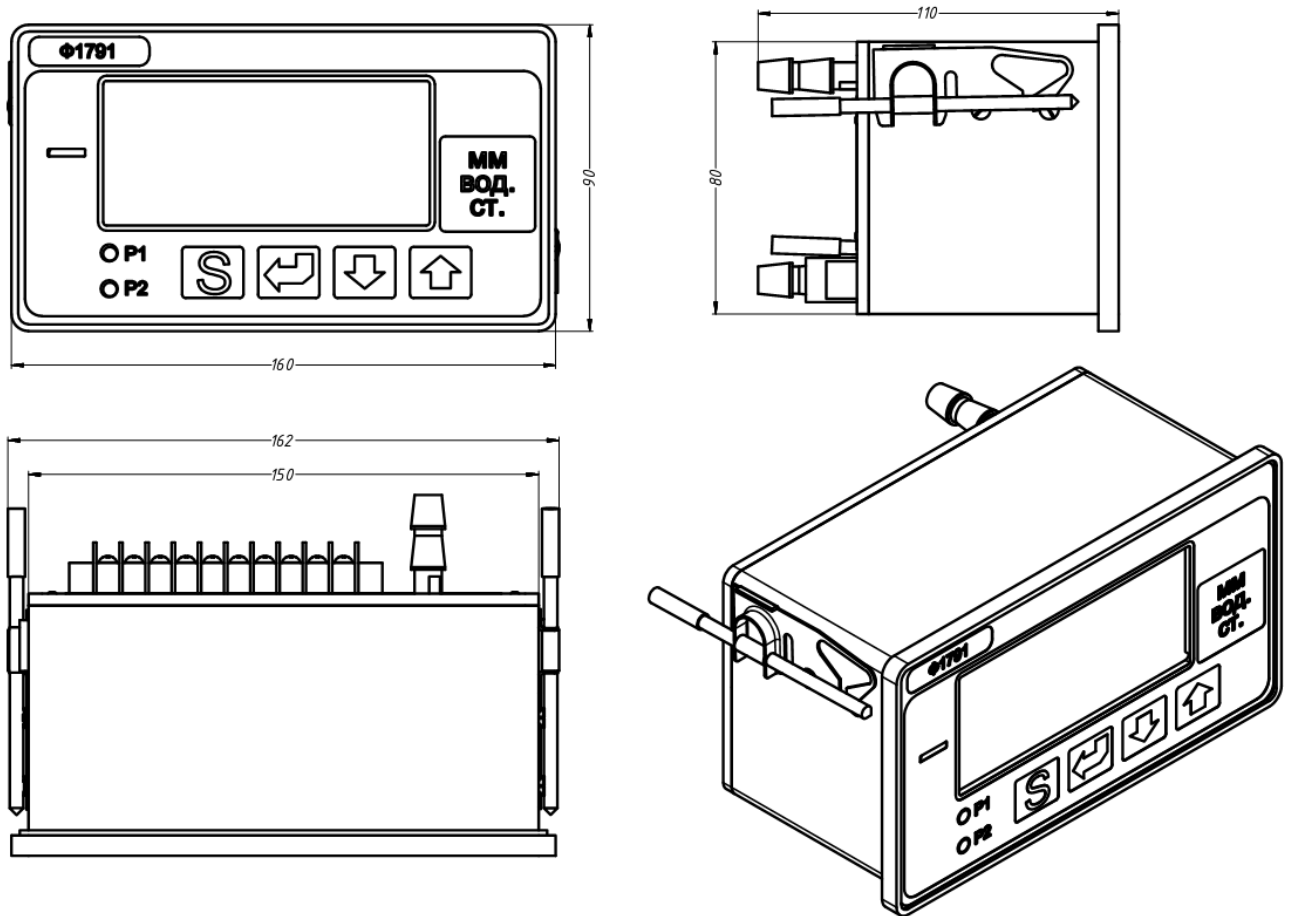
Внешний вид и габаритные размеры Ф1791.1
